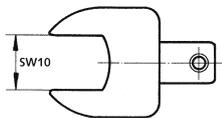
Mauleinsatz SW10 für Montage- und Drehmomentschlüssel Typ 1300A123
